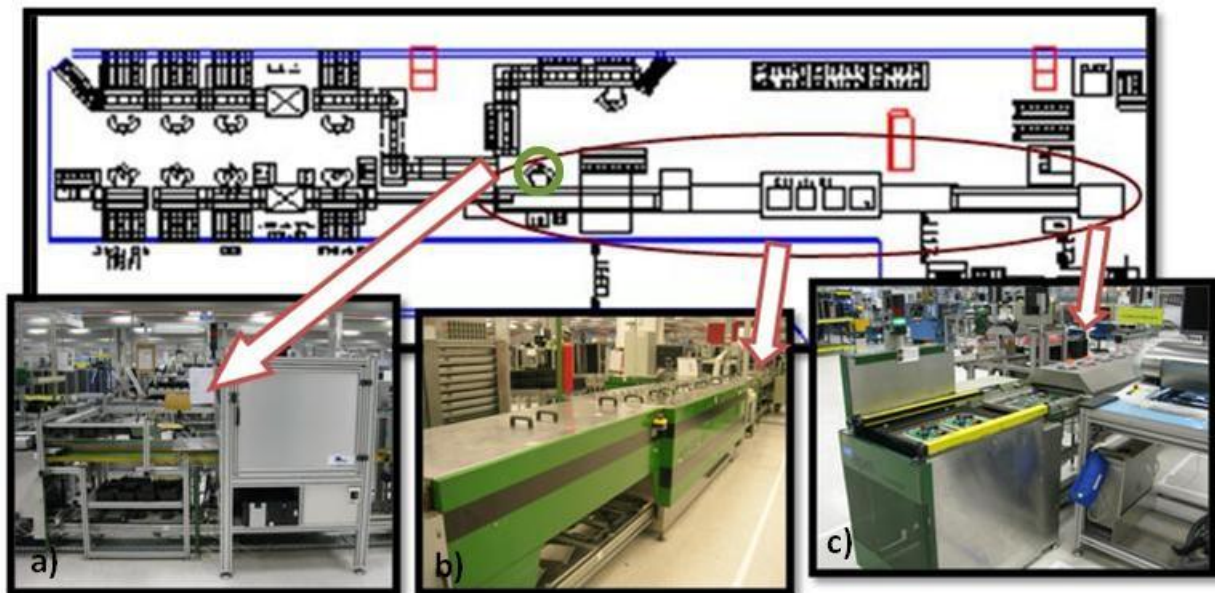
Conveyor a) Início e AOI; b) Máquina de solda; c) fim do conveyor
